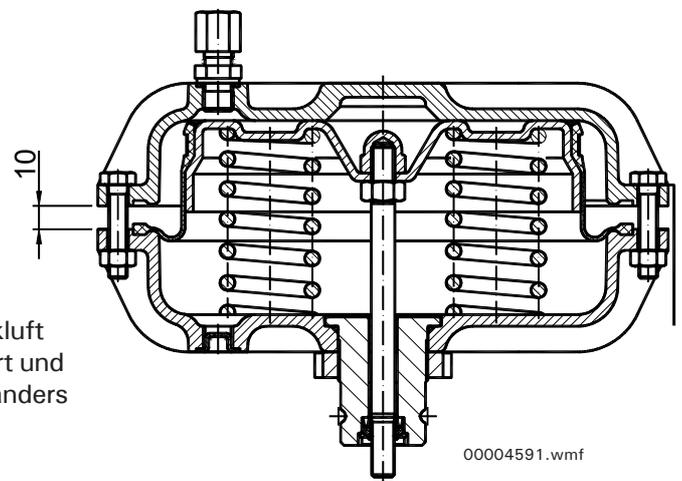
Öffnen und Schließen des Antriebsdeckels
